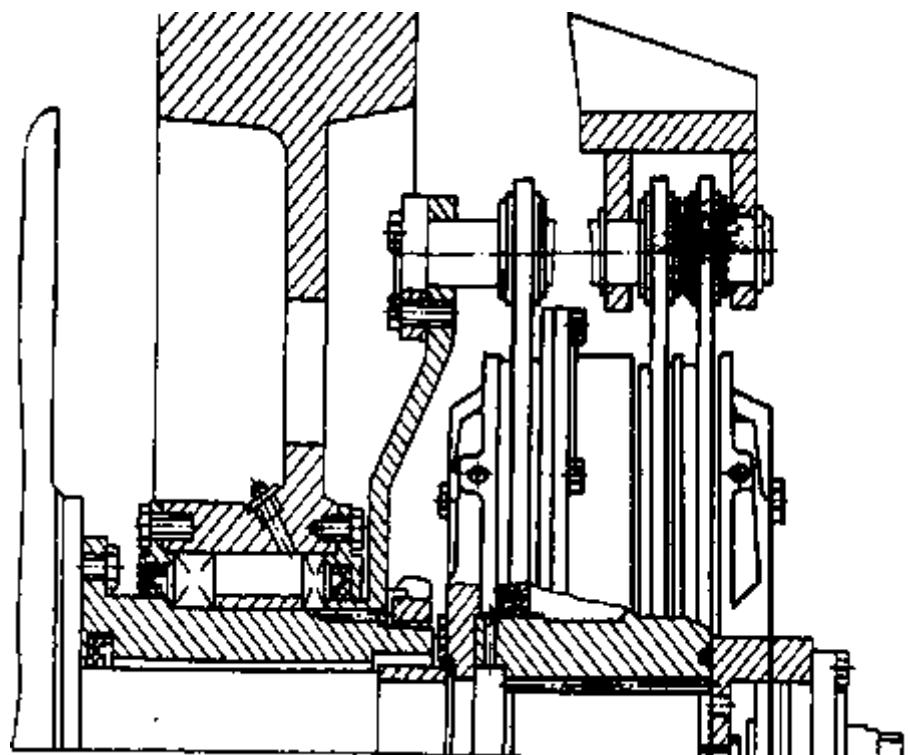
Установка муфты-тормоза на валу, разгруженном от маховика, с соединением тормозного диска со станиной через втулку
